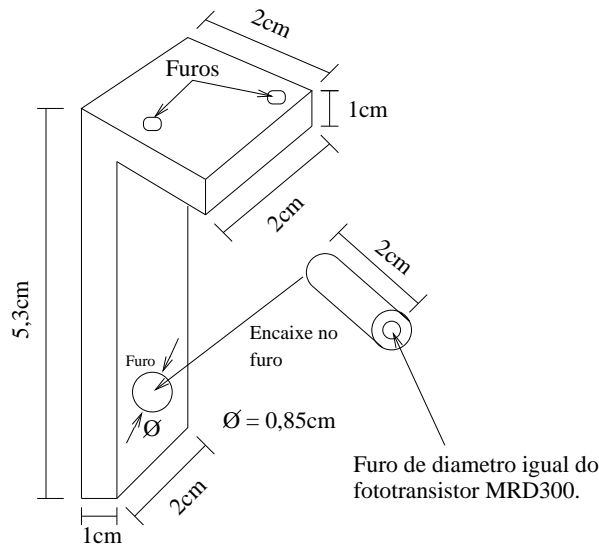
Suporte montado para fixar o fototransistor MRD300 no levitador.
